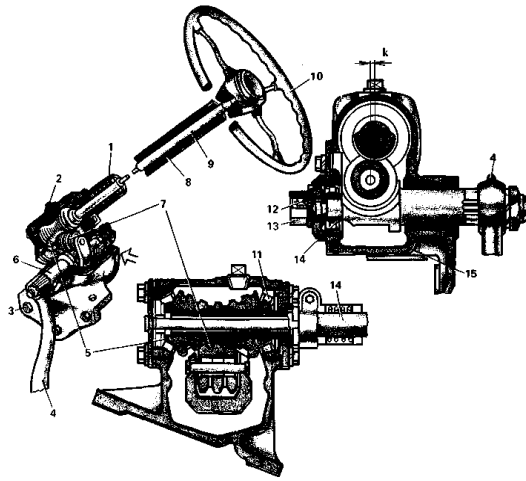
Рулевой механизм автомобиля ГАЗ-53А:
